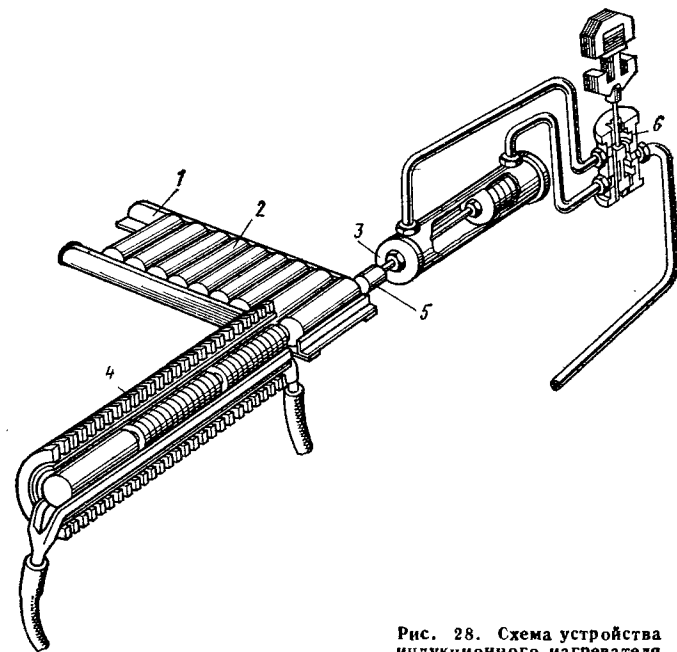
Схема устройства для загрузки индукционного нагревателя
